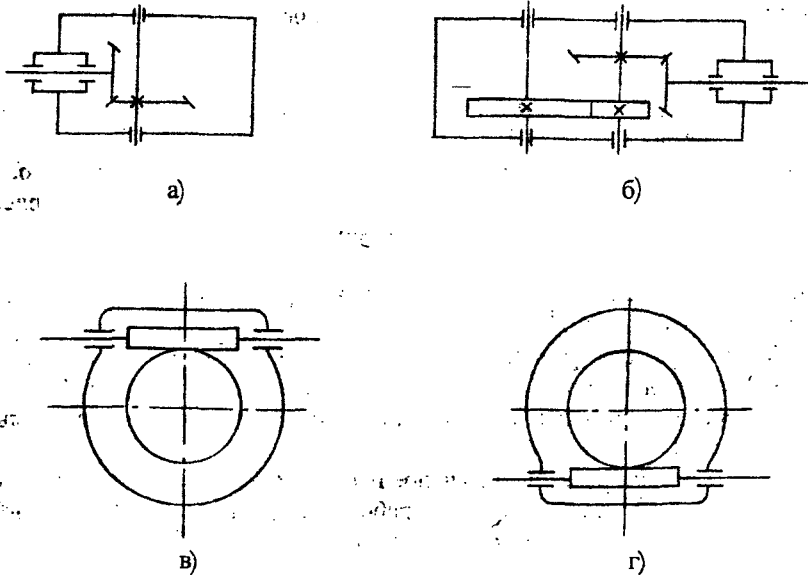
Кинематические схемы редукторов (по типу зубчатых колес)
